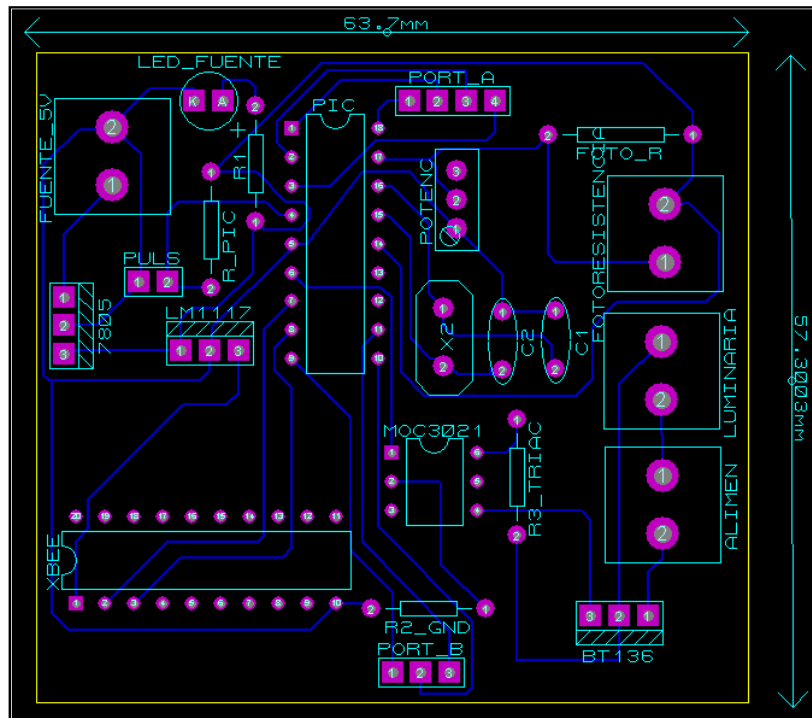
Placa impresa de la tarjeta de control para luminarias.²²⁸
